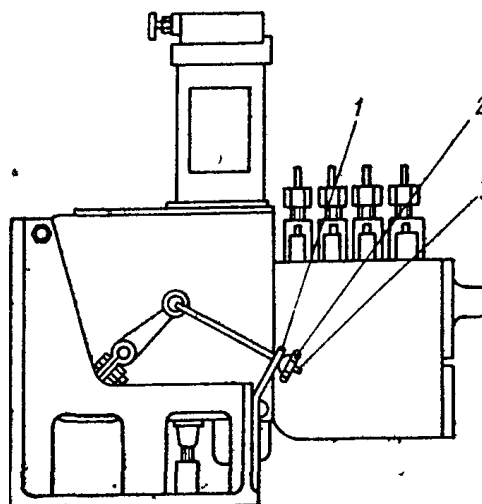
Крепление рычага регулятора топливного насоса двигателей типа Д-108 при испытаниях:
